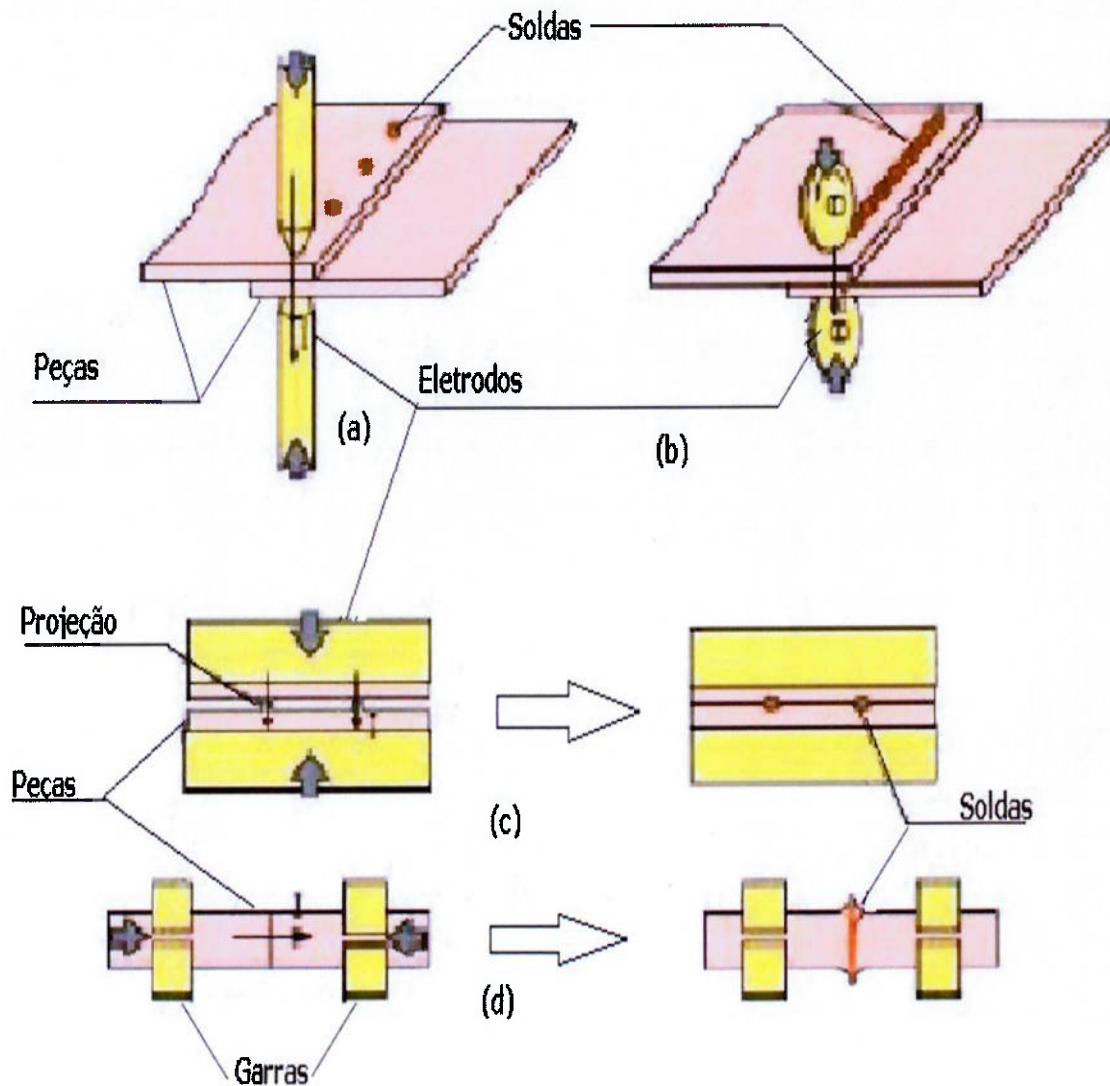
Principais tipos de soldagem por soldagem por resistência(adaptado) [8].
